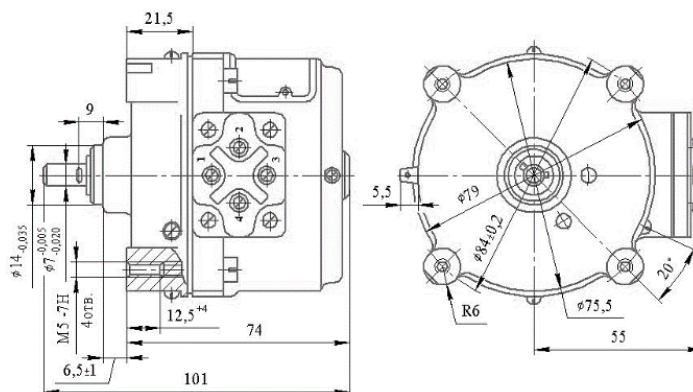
Габаритный чертеж электродвигателя РД-09
